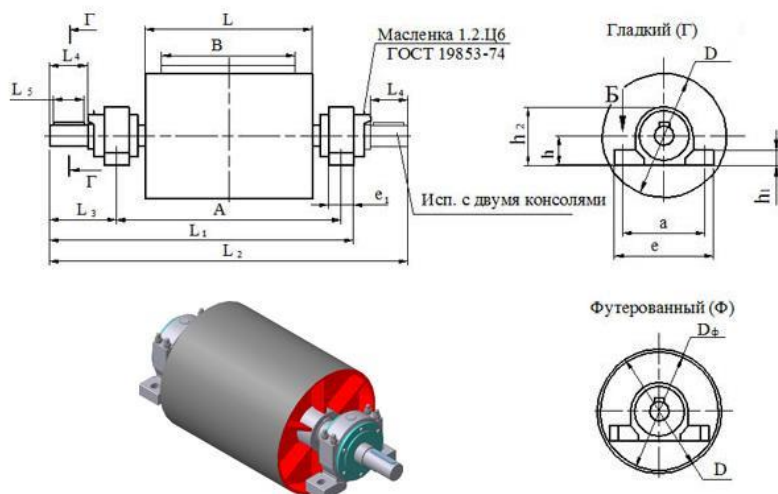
Загальний вид привідного барабану (футерованого)
